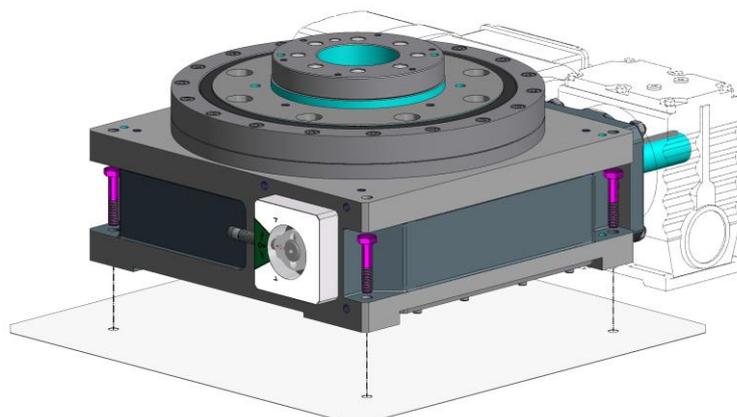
Lato montaggio RT-TT; Pagina (6) Standard
